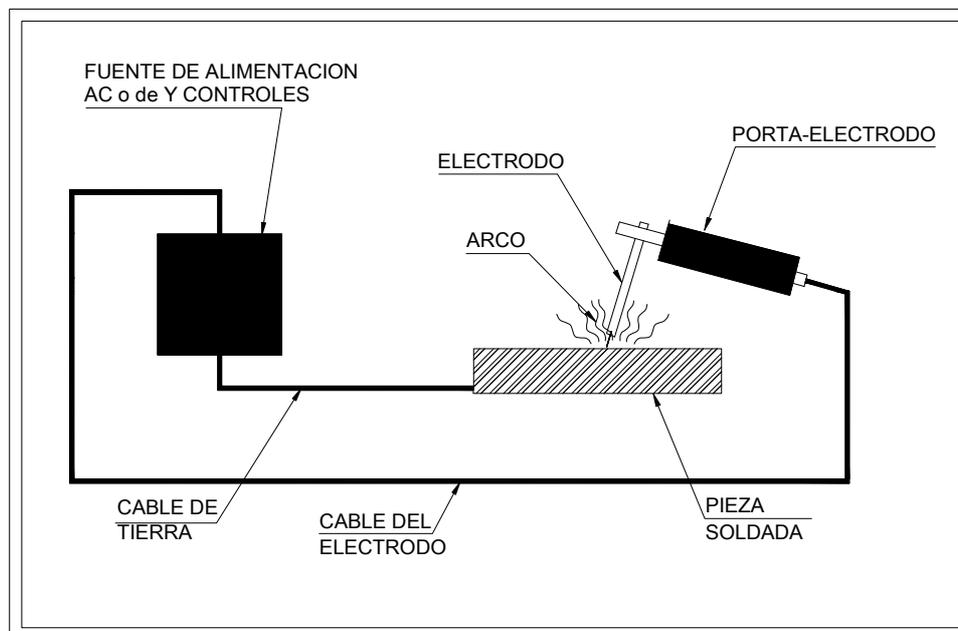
Circuito Eléctrico del proceso de soldadura al arco con electrodo revestido.
